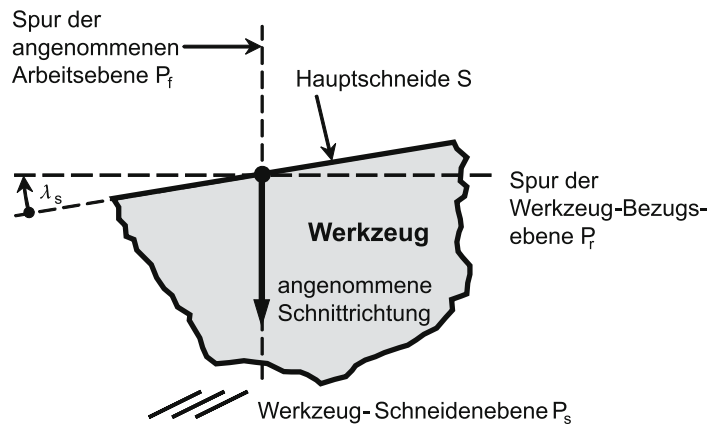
Die Lage des Werkzeug-Neigungswinkels λ_s
